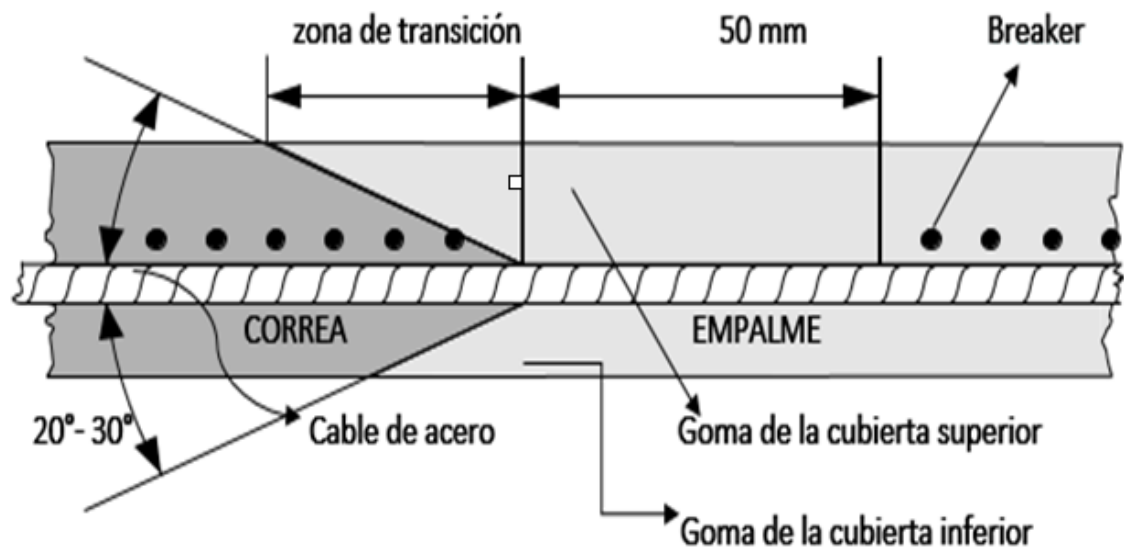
Correa de lado perfil ángulo del empalme y bisel en zona de transición.
